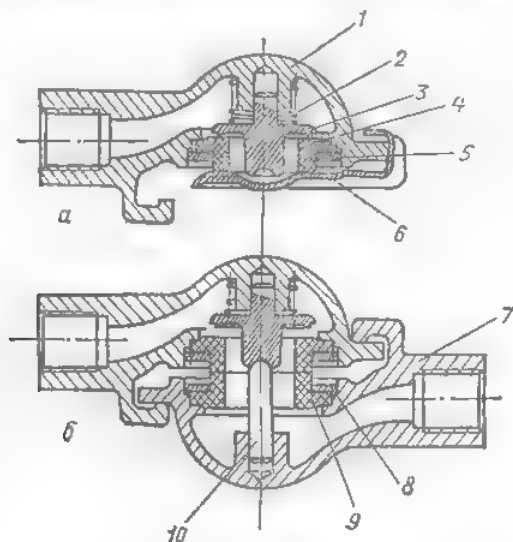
Соединительные головки однопроводной схемы привода тормоза прицепа: а — соединительная головка тягача; б — соединительные головки тягача и прицепа; 1 — корпус; 2 — пружина; 3 — обратный клапан; 4, 9 — уплотнительные прокладки; 5, 8 — кольцевые гайки; 6 — крышка; 7 — корпус; 10 — штифт
